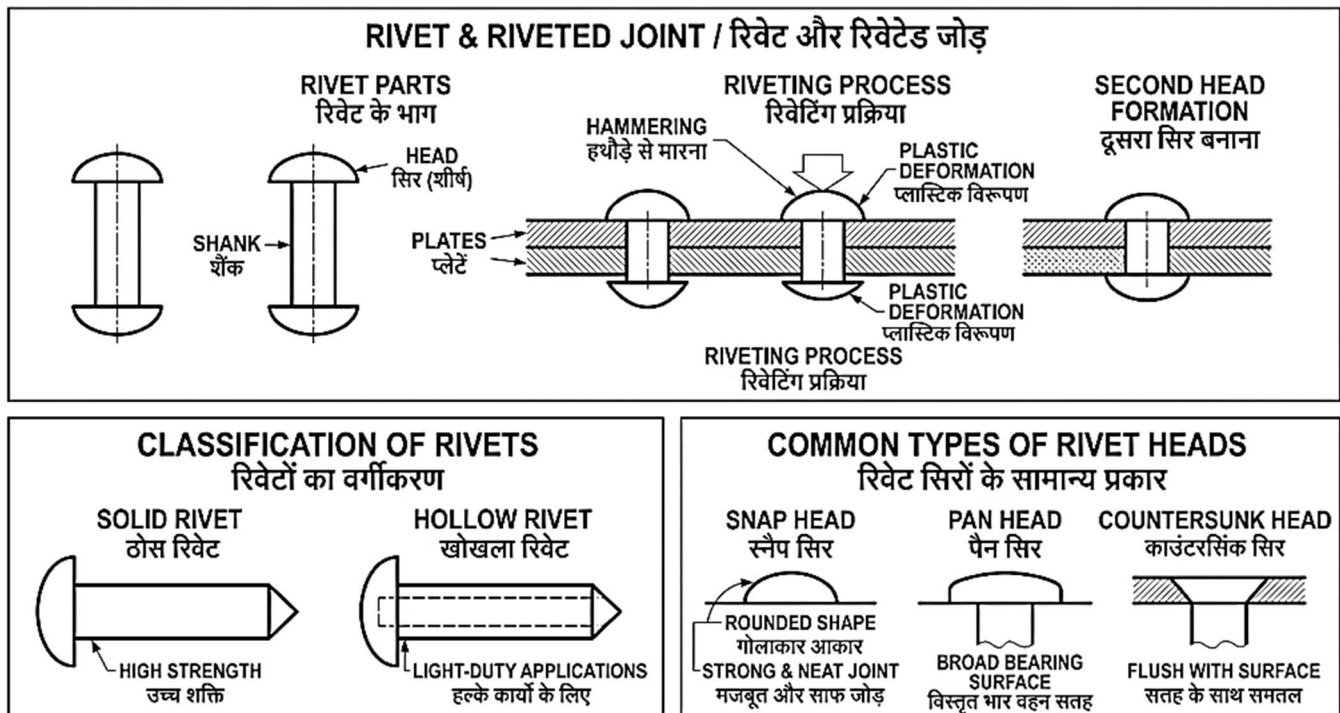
Rivet Parts, Riveting Process, Classification and Types of Rivet Heads | रिबेट के भाग, रिवेटिंग प्रक्रिया, वर्गीकरण एवं रिबेट हेड के प्रकार
